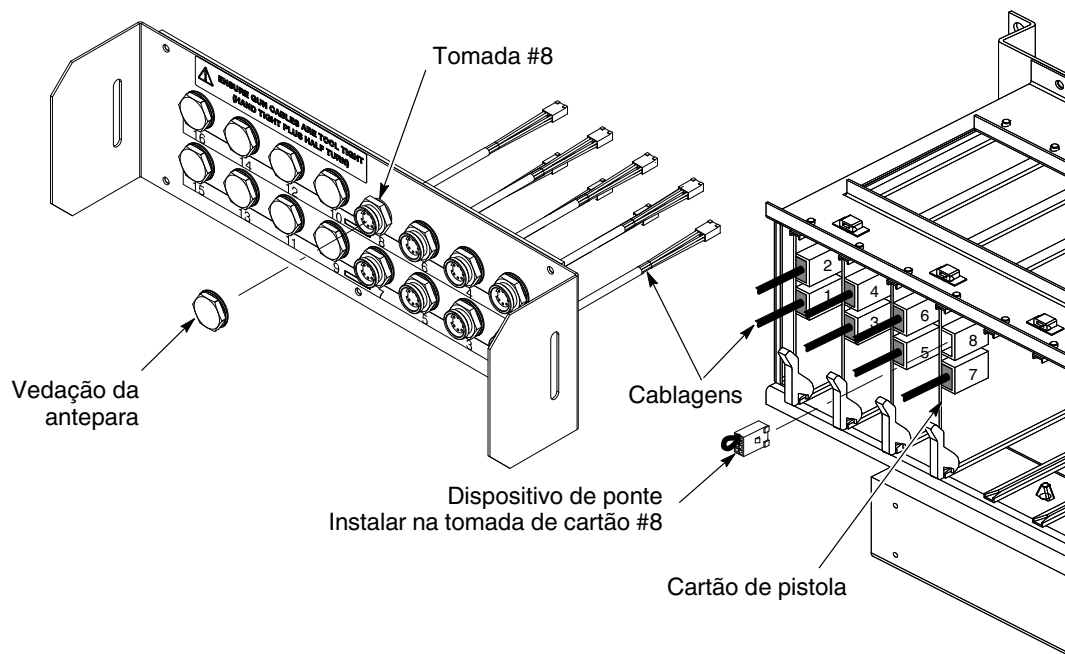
Instalação de vedações e fios de ponte - Exemplo mostrando um sistema de 8 pistolas utilizando 7 pistolas
